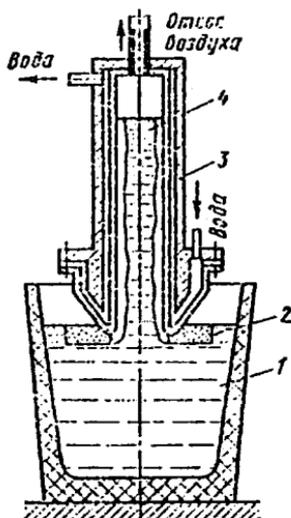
Установка для литья вакуумным всасыванием: 1 — металл; 2 — плоское кольцо; 3 — литейная форма; 4 — отливка
